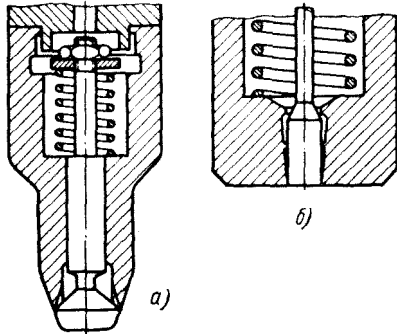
Клапанная форсунка с кольцевым распиливающим отверстием:
